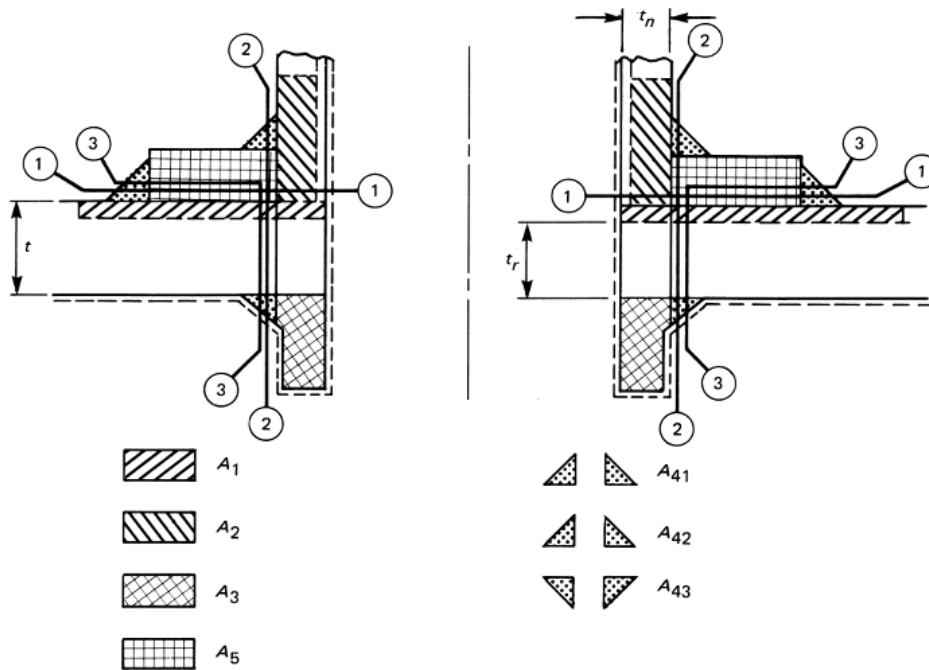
Cargas de la soldadura para la fijación de la boquilla y trayectorias de resistencia de soldadura, (UG-41.1), (ASME, 2013)
